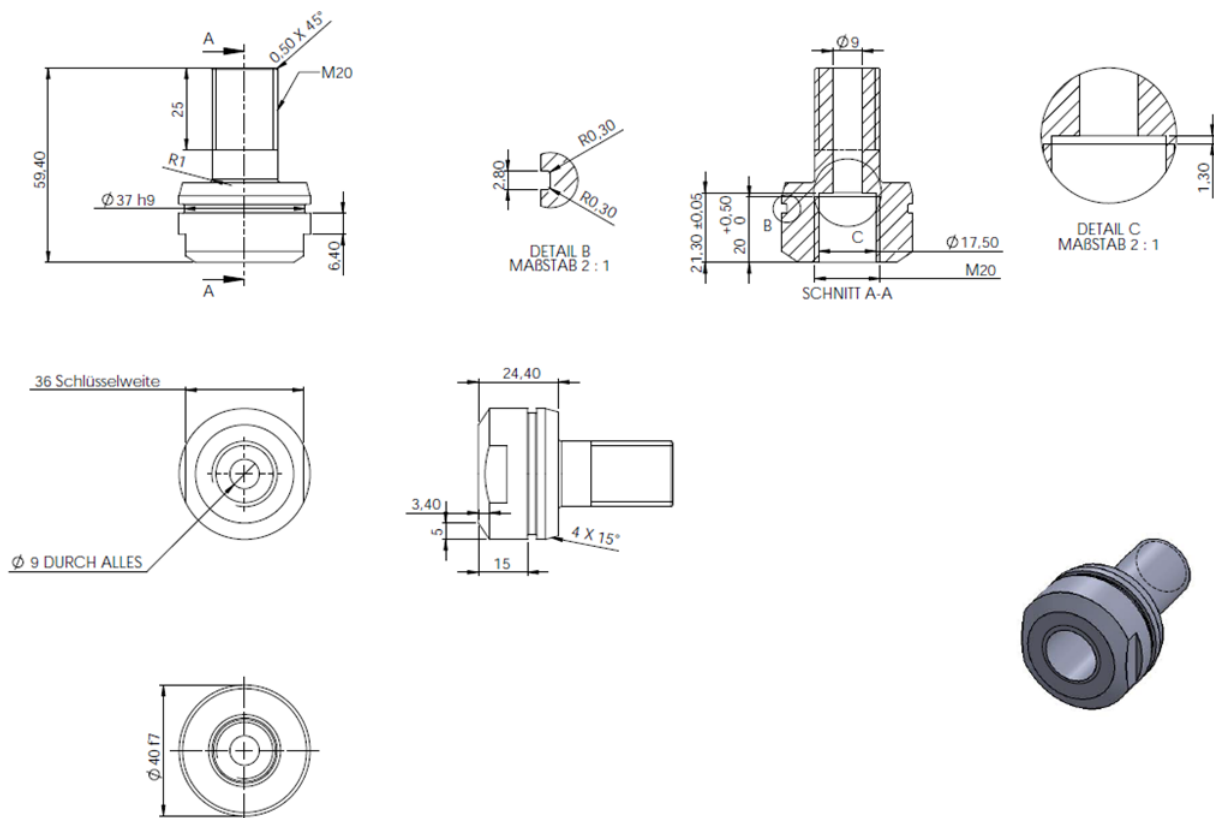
Kolbenstange Endstück oben mit Angaben in mm.
